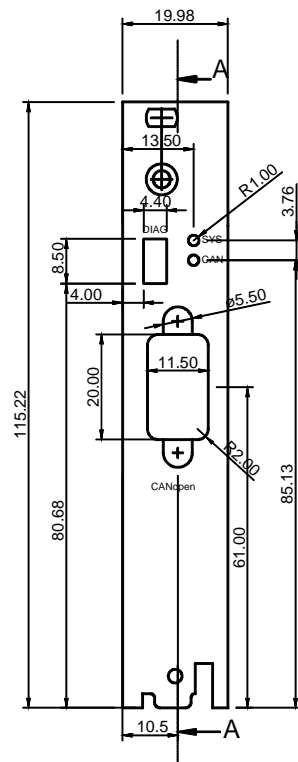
Abmessungen Frontblende für CIFX 80-CO
